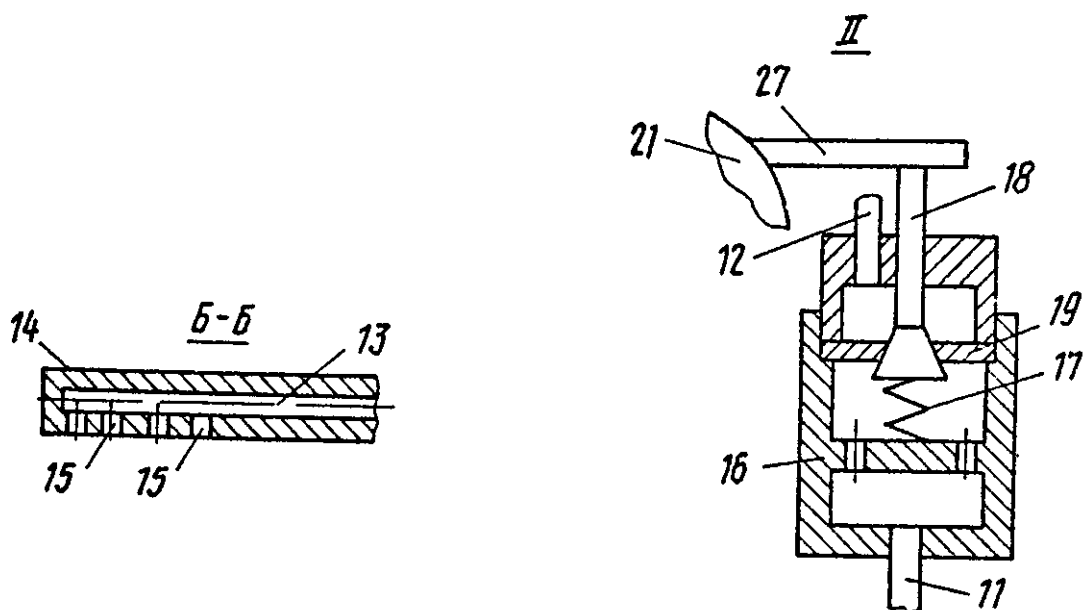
Розріз пружинного пальця і запірно-регулювальний пристрій
